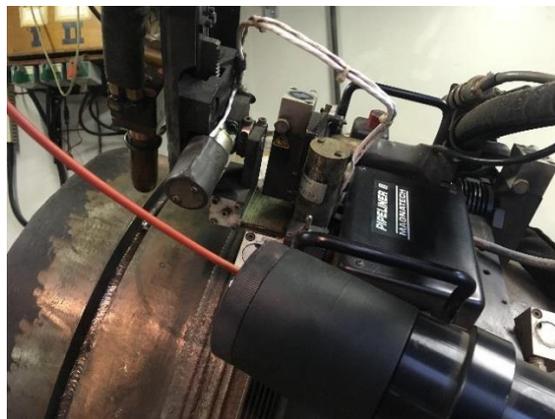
Sistema de soldagem orbital pipeliner II da empresa Magnatech
